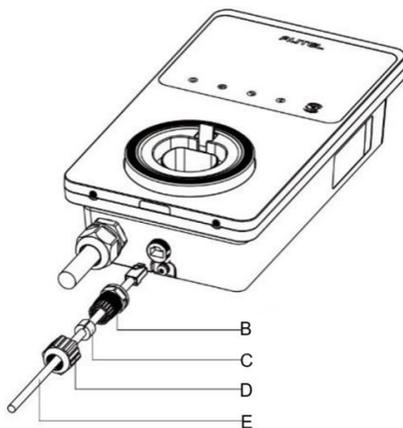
Installazione del pressacavo Ethernet impermeabile
